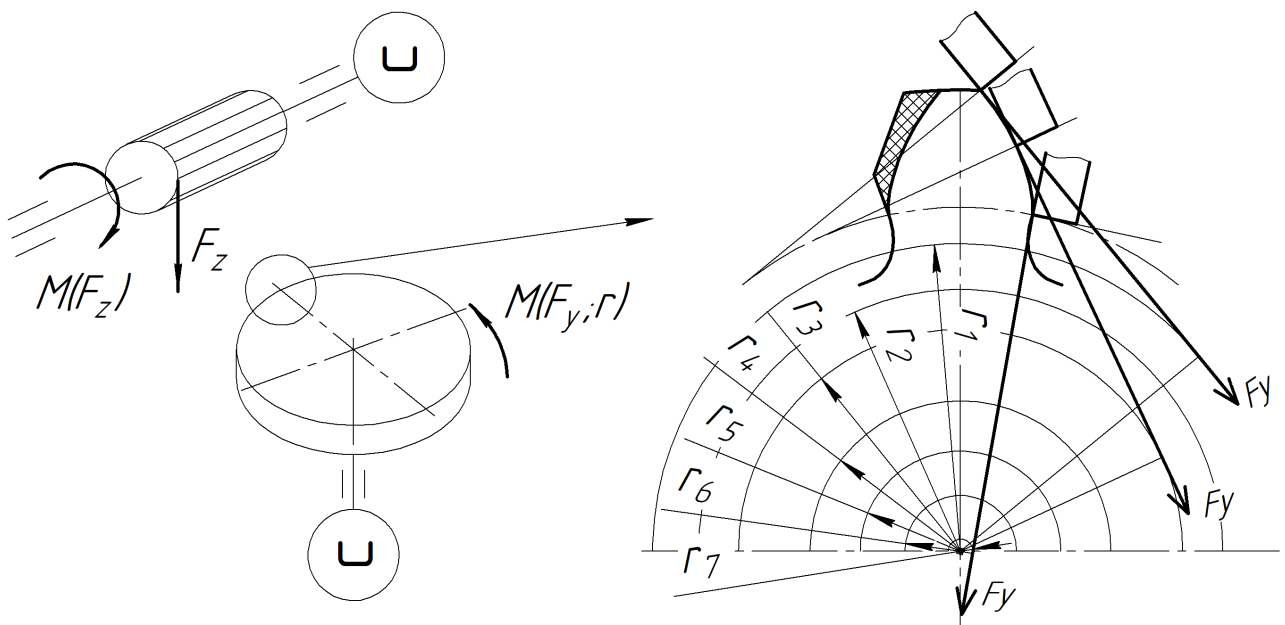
Схема утворення моментів при черв'ячно-контурному зубофрезеруванні
